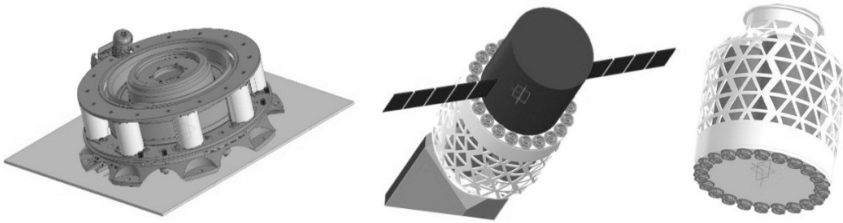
Части 3D-модели: СПД-230, ферма с баками и двигателями
